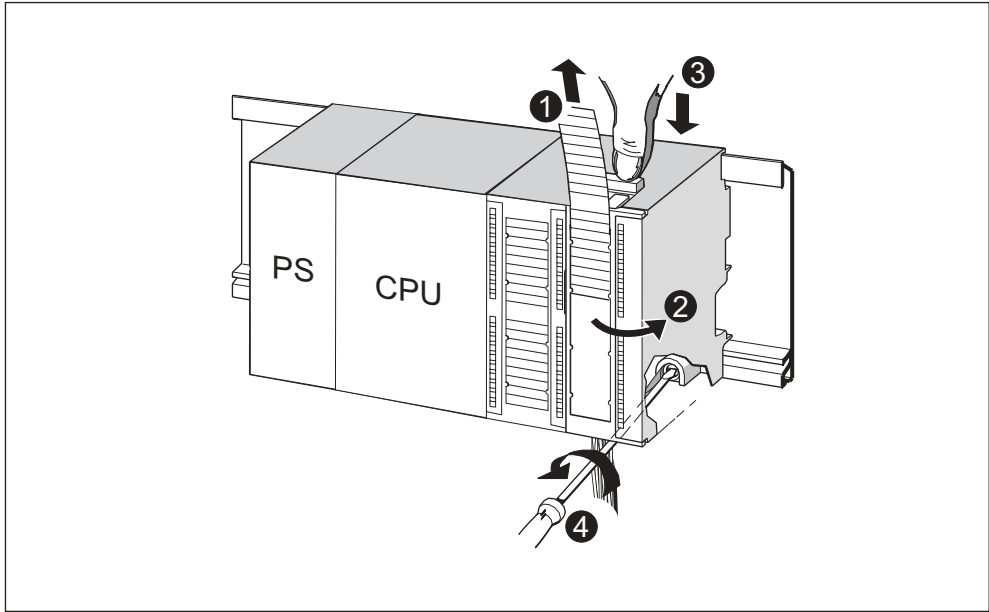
Extracción del conector frontal y desmontaje del módulo
